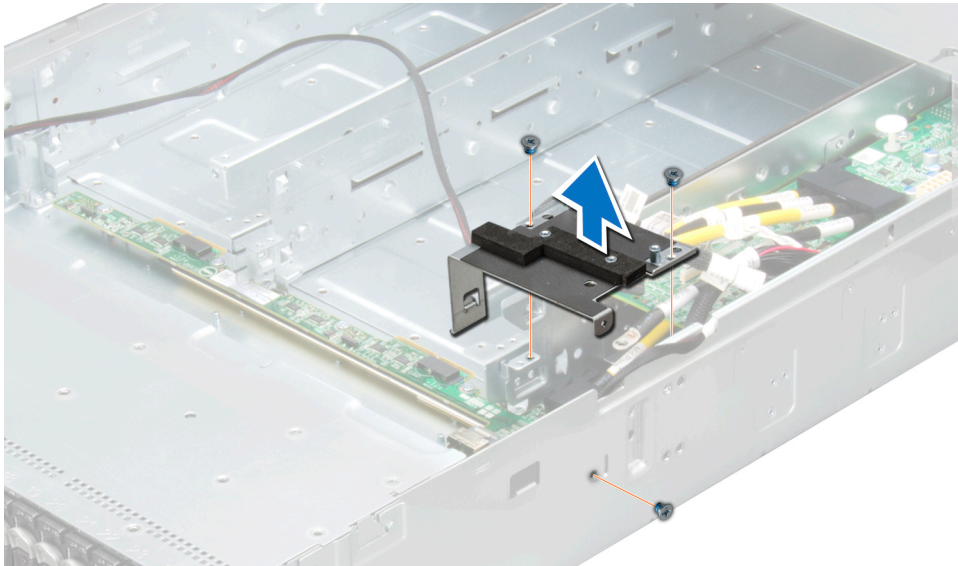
Retrait du support de la barre de fixation de fond de panier central
